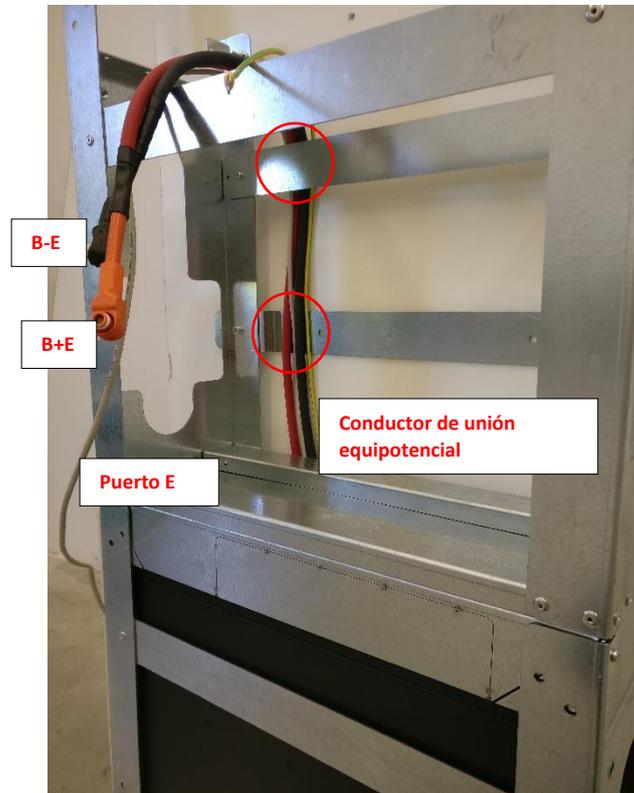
Colocación de los conductores de conexión entre el WALL-BOX-Bx BASE y extensión del WALL-BOX-Bx
